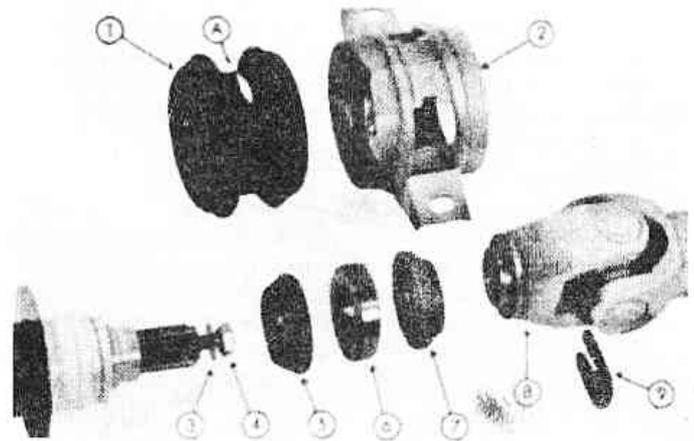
Детали подшипника средней опоры (Разд.3)
